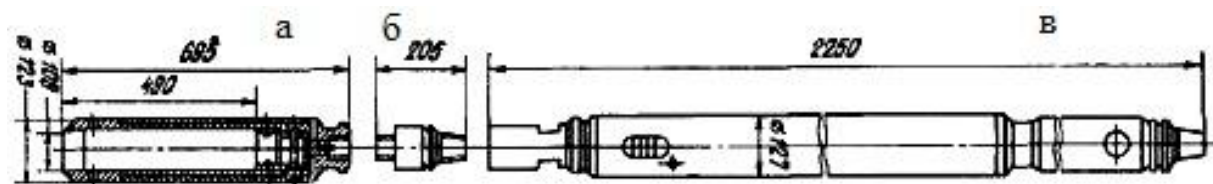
Снаряд для отбора грунта грунтоносом: а – грунтонос ГК-3, б – переходник, в – ударный патрон.
